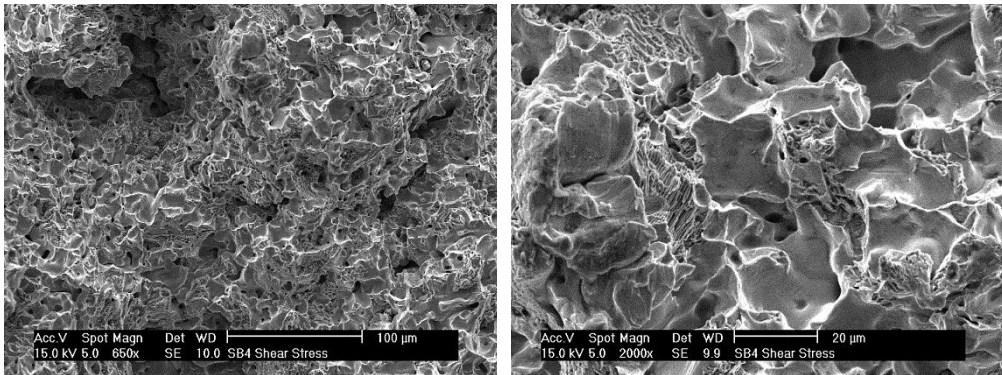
13. Superficie de fractura del sustrato (izquierda) y detalle (derecha).
